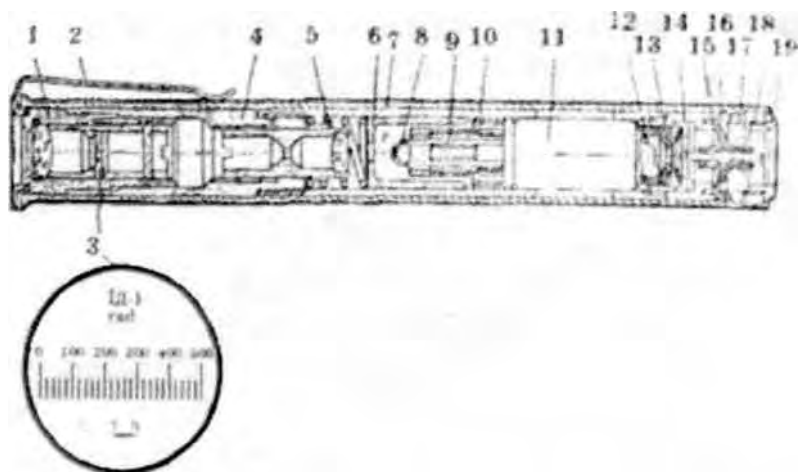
Будова дозиметра ІД-1: 1 - окуляр; 2 - пружина; 3 - тримач; 4 - об'єктив; 5 - пружина; 6 - електрод зовнішній; 7 - корпус; 8 - електрод внутрішній; 9 - пружина; 10 - електрод центральний; 11 - конденсатор; 12 - вивід; 13 - обмежувач; 14 - контакт; 15 - діафрагма; 16 - кільце; 17 - гайка; 18 - захисний ковпачок; 19 - ковпачок зарядного гнізда
